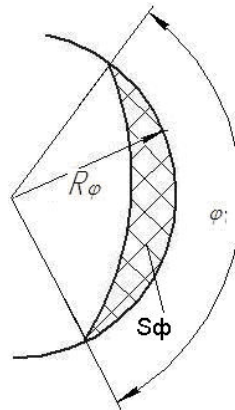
Расчетная схема фильтрующего элемента
